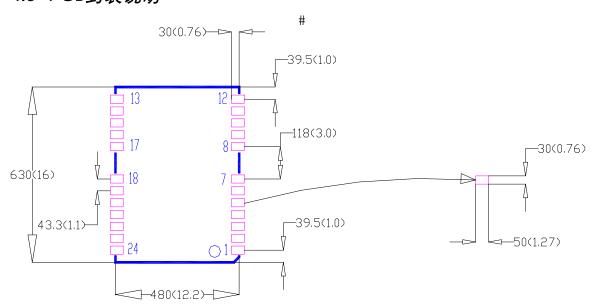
UM220-III N 推荐 PCB 封装设计(尺寸单位: mil, 括号内单位: mm)
